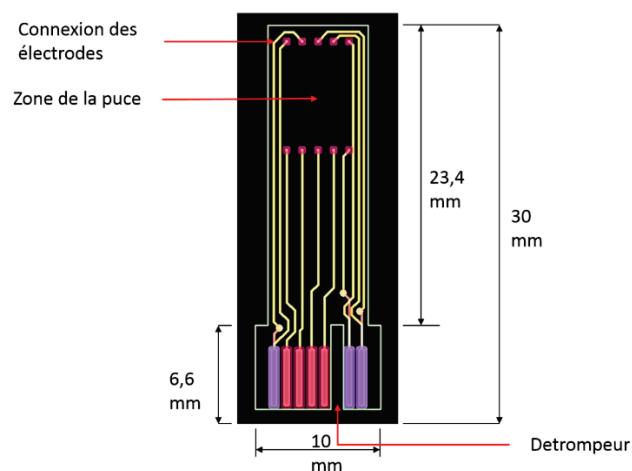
Design du PCB – en rouge contact en face avant – en violet contact en face arrière
